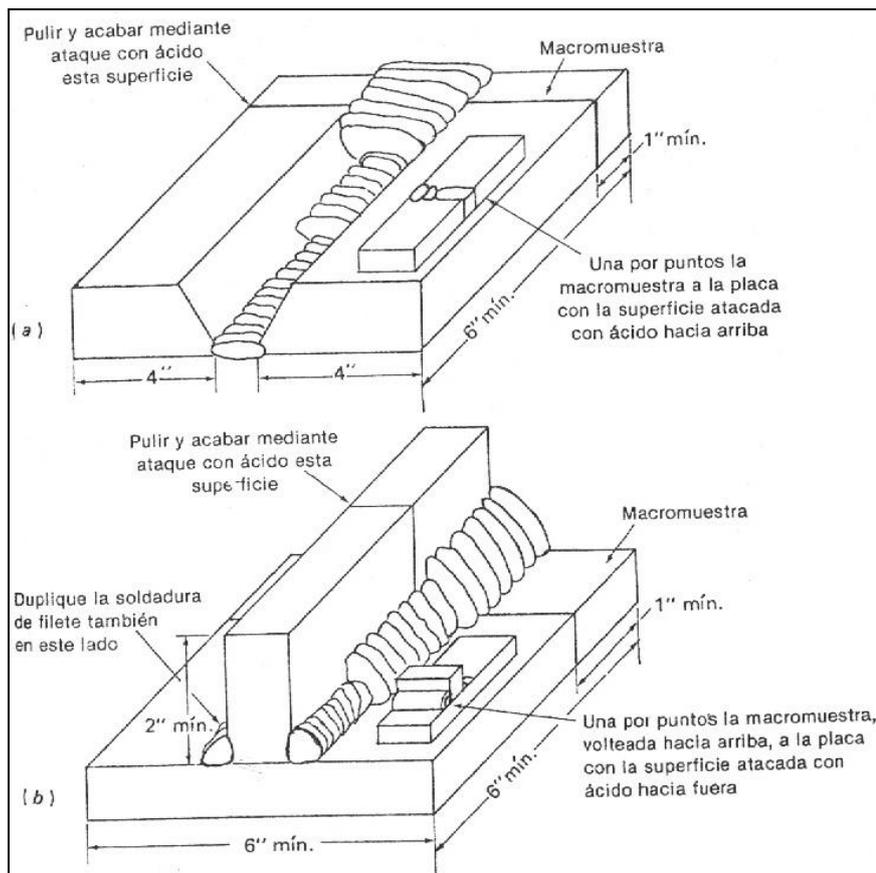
Normas relativas a la mano de obra de aplicación. a) Soldaduras de ranura; b) Soldaduras de filete
